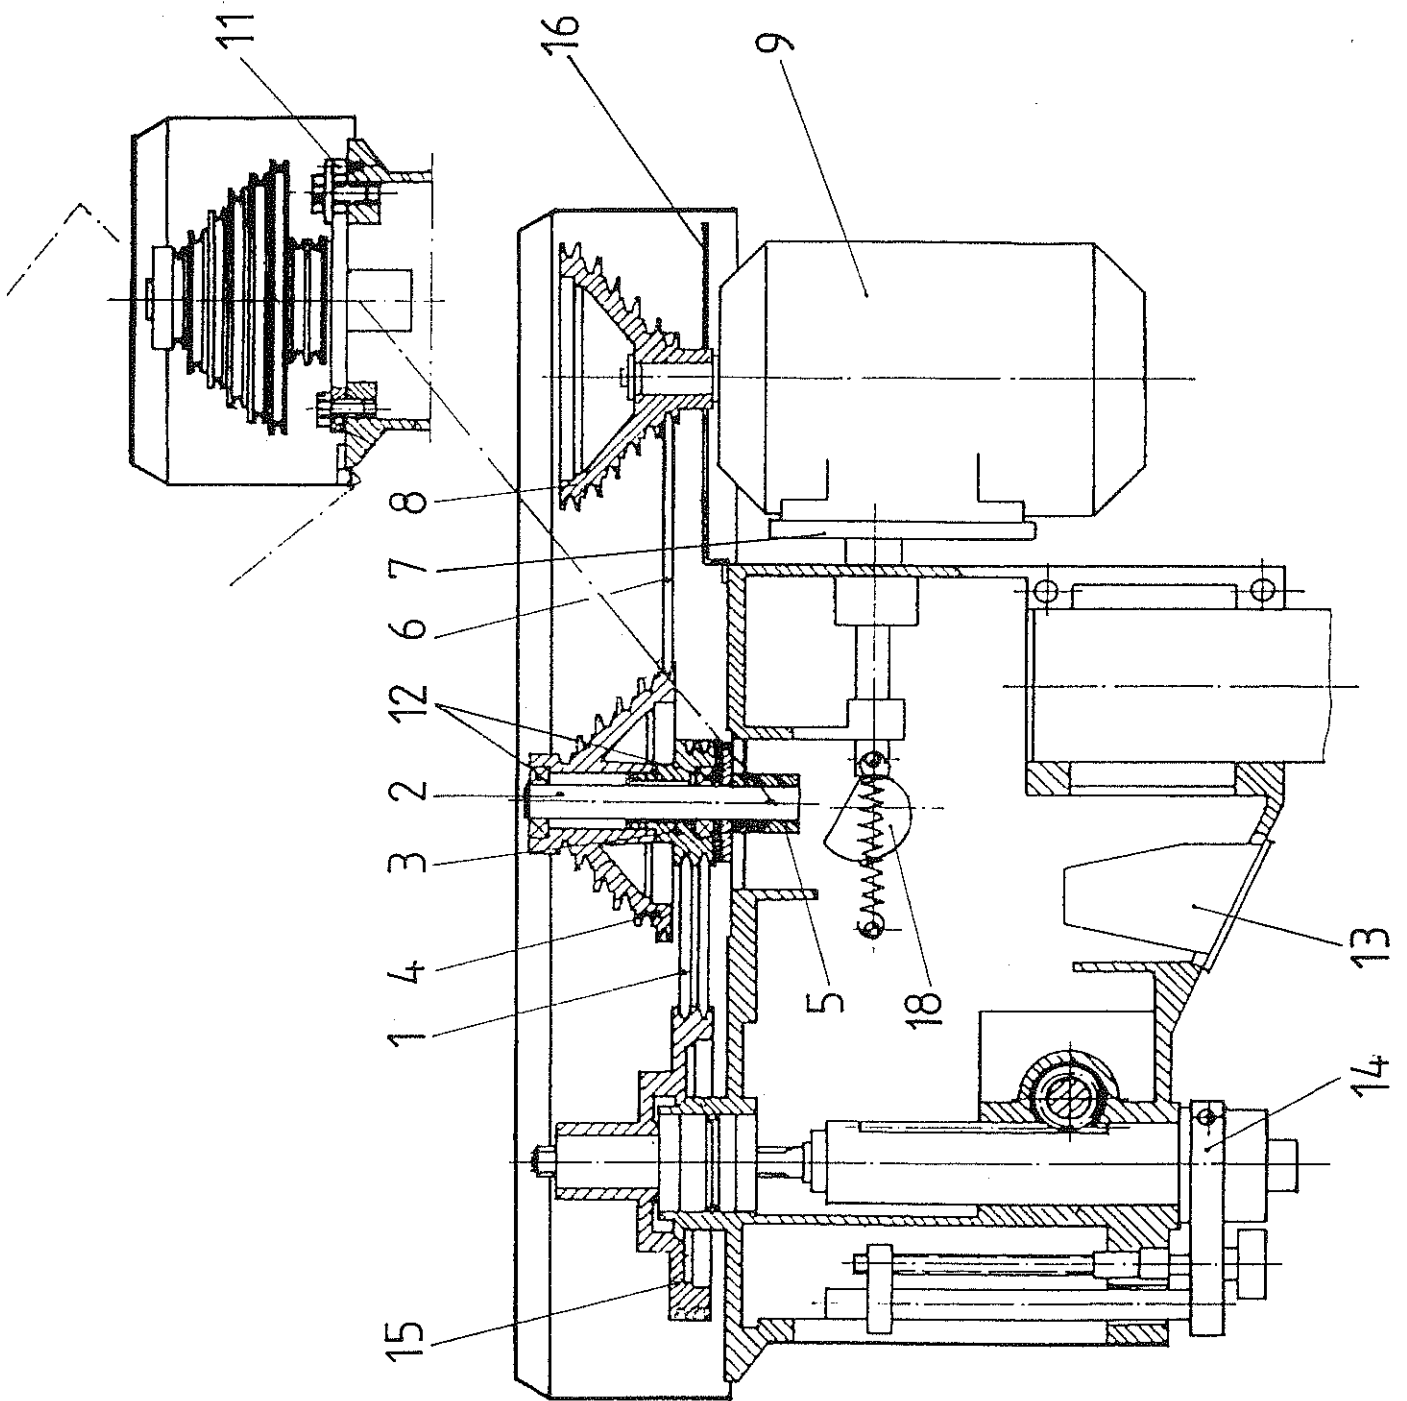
/figure 5: Bohrkopf / drilling head 25
